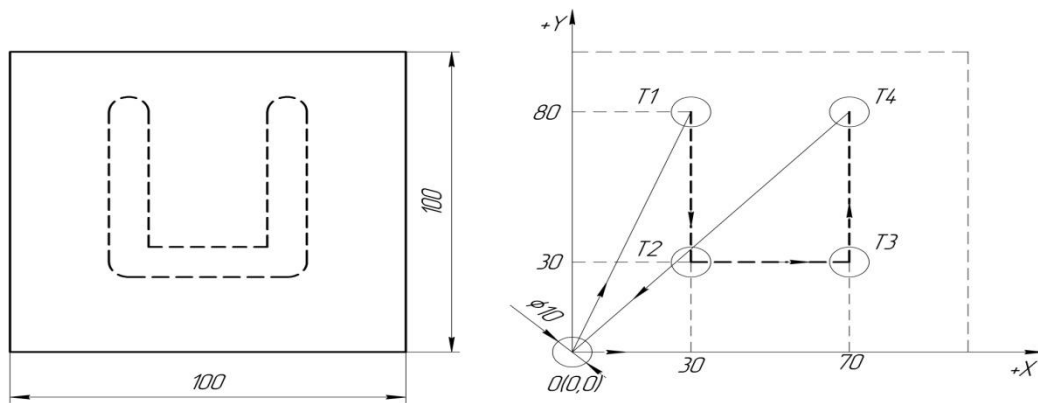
Ескіз заготовки та розташування її в прямокутній системі координат
